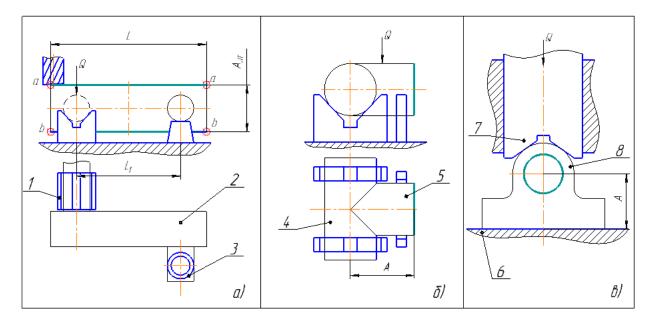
Схемы установки заготовок: а – кривошипа; б – тройника; в – корпуса подшипника
